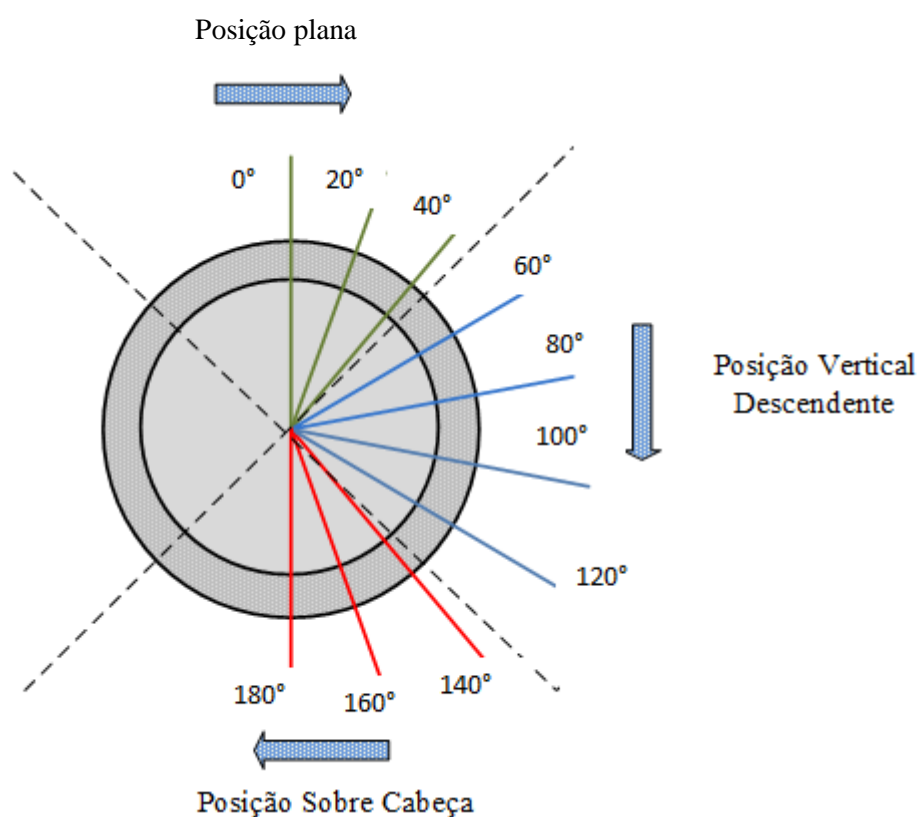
Divisão do tubo de acordo com a posição de soldagem.
